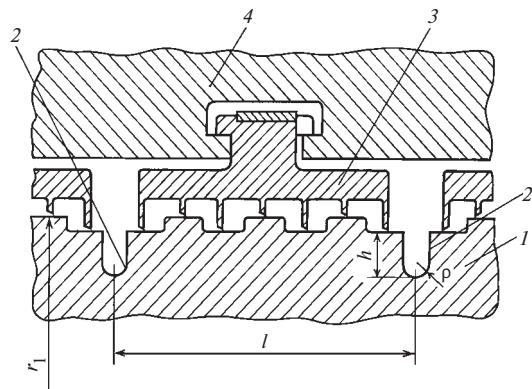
Схема участка вала с разгрузочными канавками:
